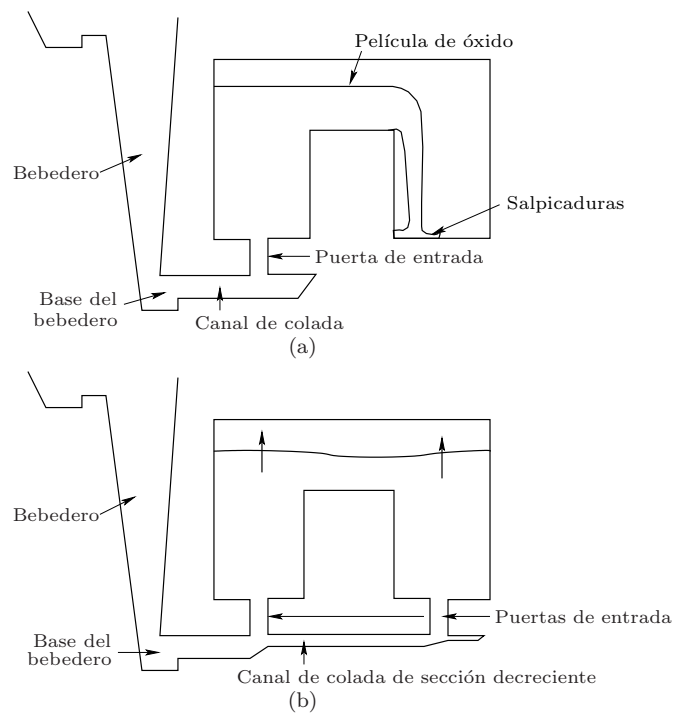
Esquema del llenado de una pieza. a) Sistema con una puerta de entrada. b) Sistema con dos puertas de entrada.
